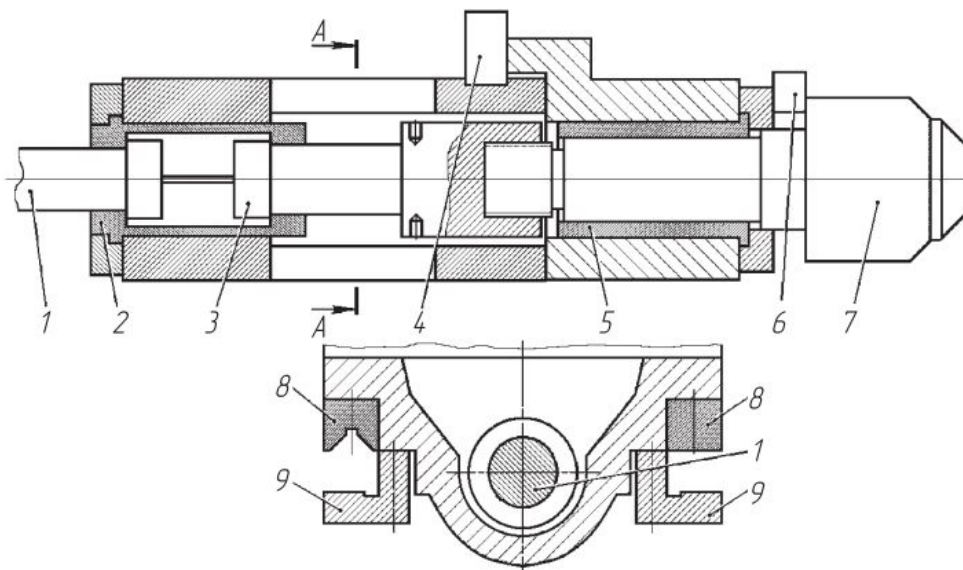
Рабочие салазки горизонтально-протяжного станка модели /А545:
